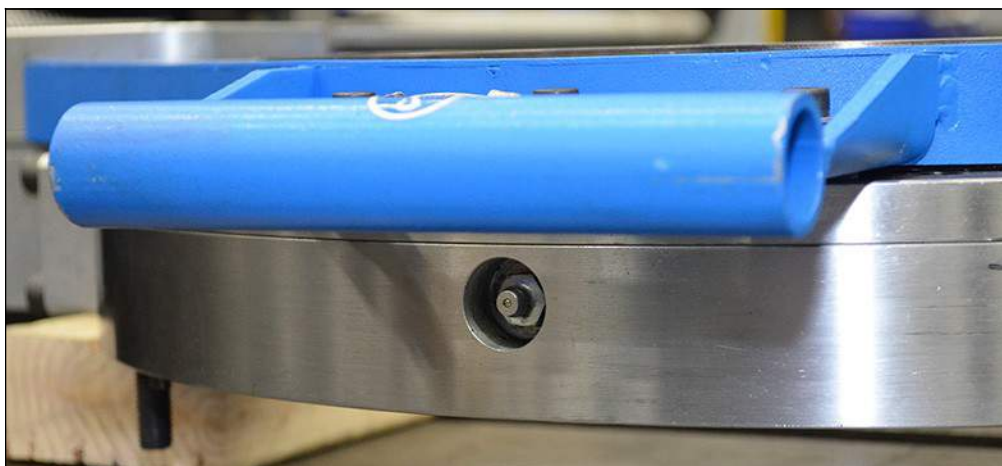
RDU CON RODAMIENTO ENGRASADOR
